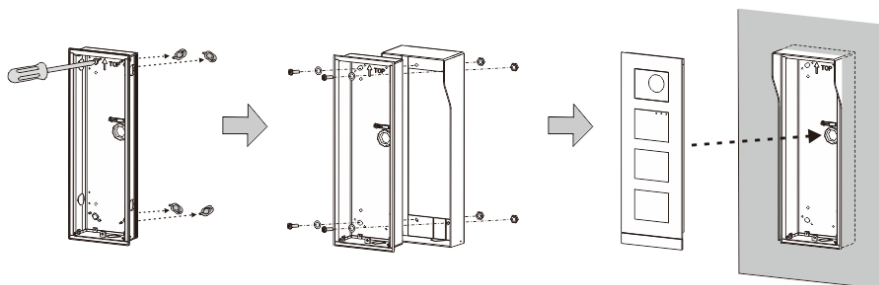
Montaggio a incasso con copertura di protezione contro la pioggia
